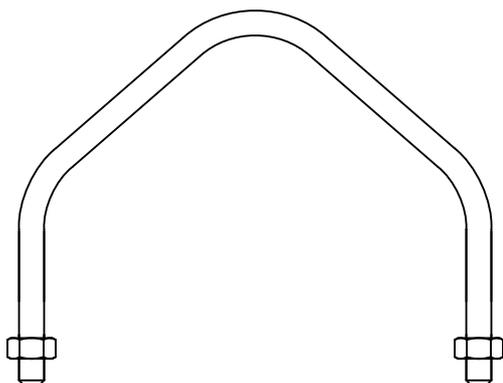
Kit support de montage mural ou sur tuyau (B2)
